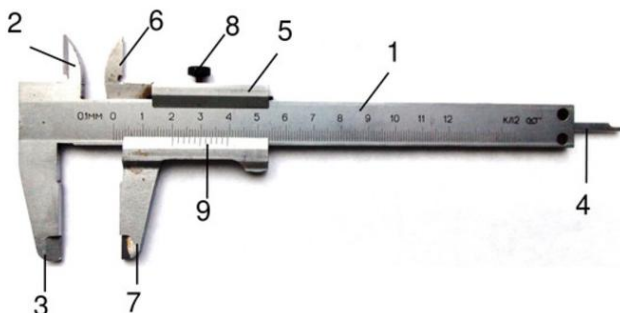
Штангенциркуль з ноніусом: 1 – штанга, 2 – нерухома верхня губка, 3- нерухома нижня губка, 4 – глибиномір, 5 – рамка, 6 – рухома верхня губка, 7 - рухома нижня губка, 8 – затискний гвинт, 9 - ноніус
